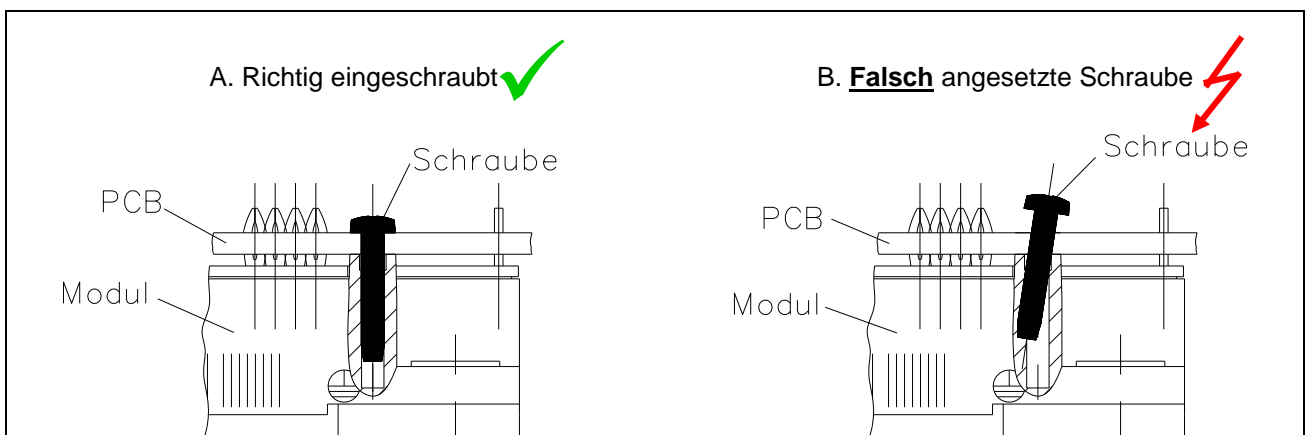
PCB Befestigungsdome beim EconoPACK™ Modul
